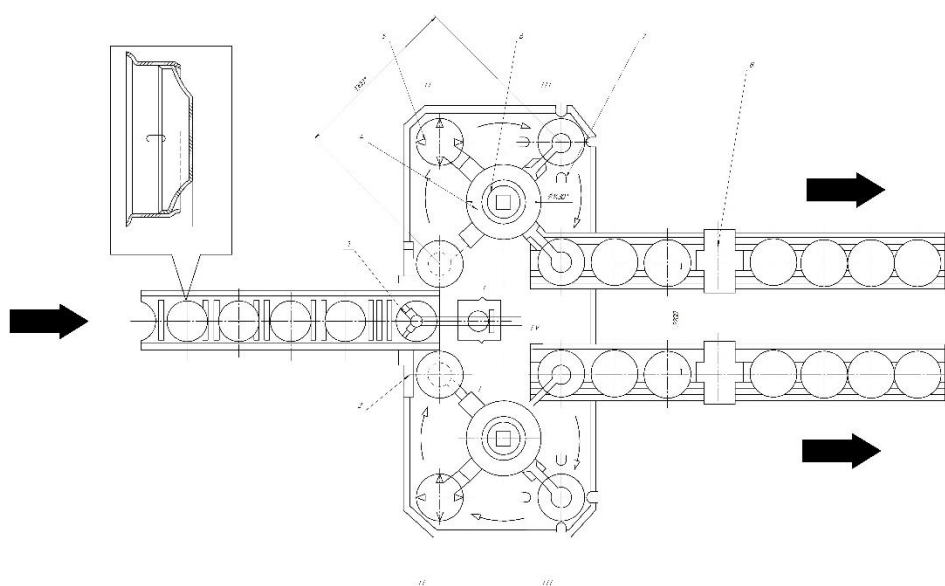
Схема багатопозиційної установка автоматичного складання колеса
